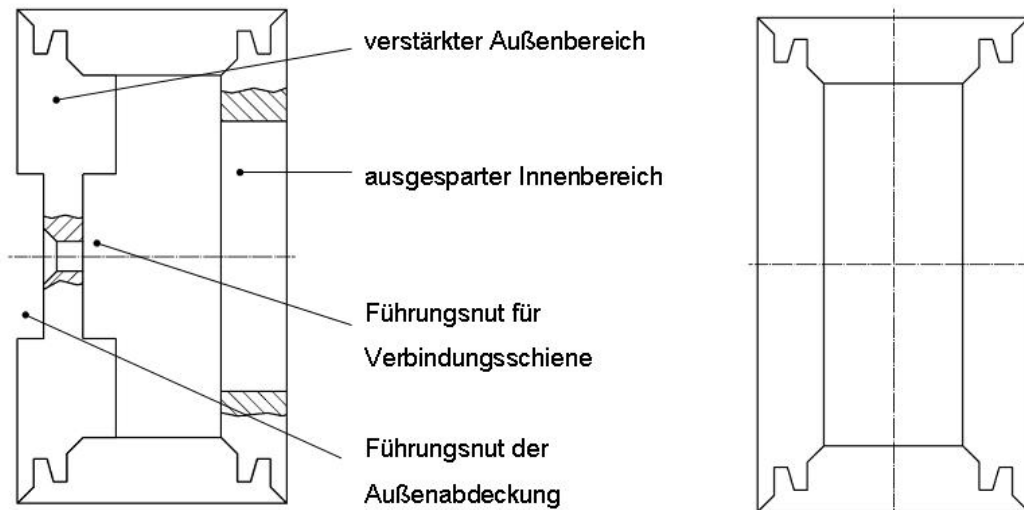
Modifiziertes Rollenbahnprofil und Grundprofil im Vergleich
